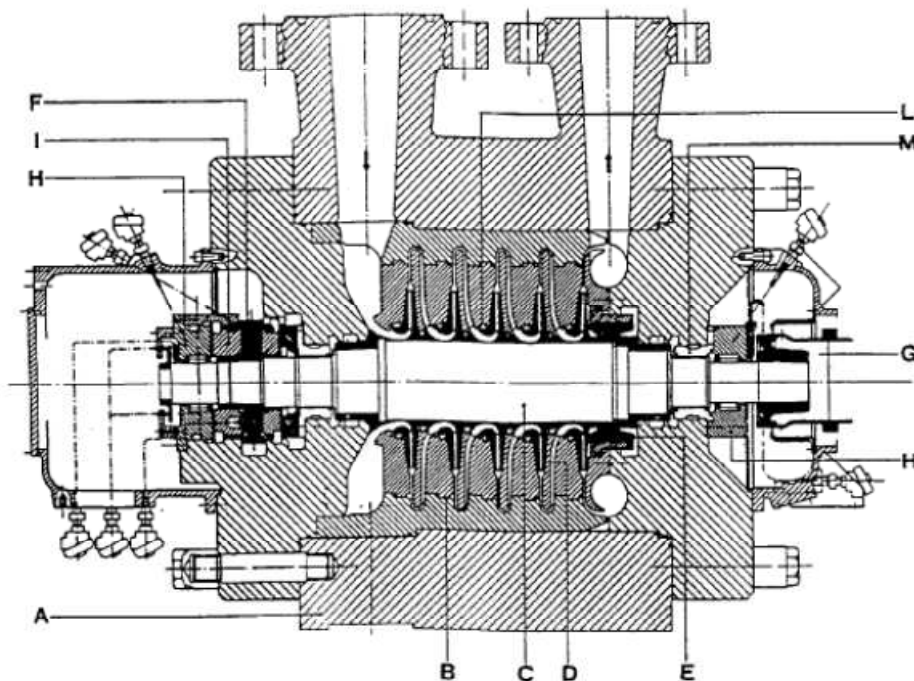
Vista em corte de compressor centrífugo (Fonte: Compressor Handbook, Paul C. Hanlon)
